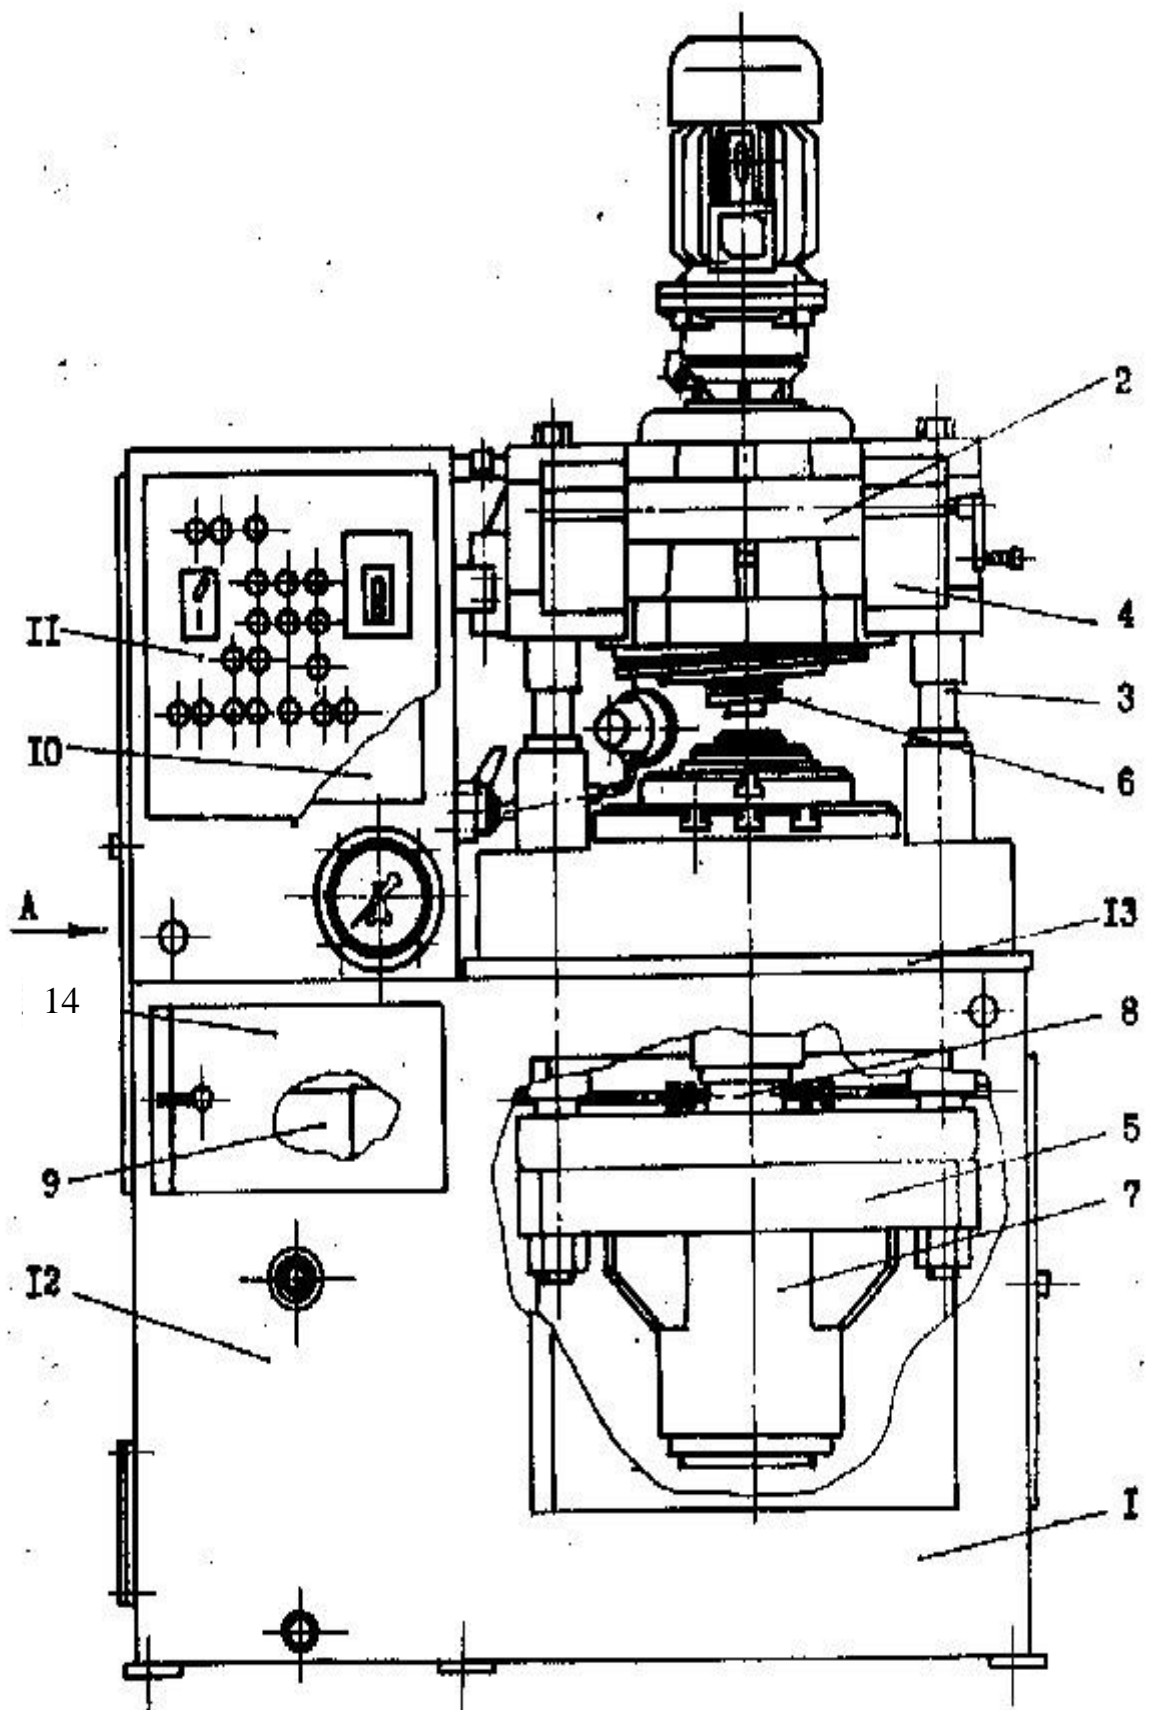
Фронтальний вид преса ПДШО – 280/30
